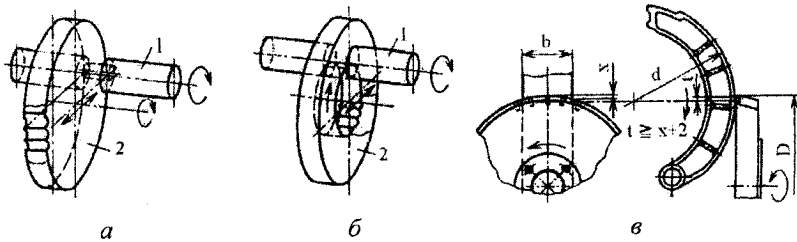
Обробка циліндричних поверхонь: *а* – дисковою фрезою з зубами на зовнішній циліндричній поверхні; *б* – дисковою фрезою з зубами на внутрішній циліндричній поверхні; *в* – торцевою фрезою з широкими торцевими різальними кромками; 1 – деталь; 2 – фреза
